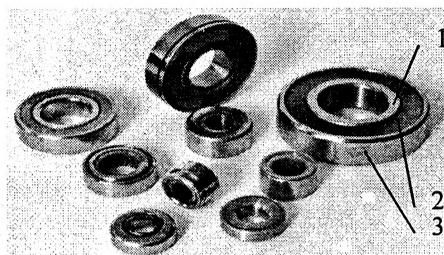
Различные типоразмеры подшипников скольжения на основе древесины
